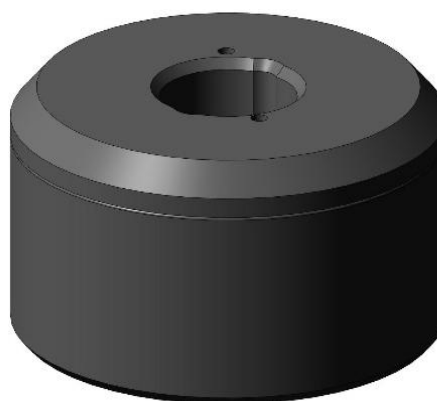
3D модель корпуса прессовой оснастки для прессования дугового канала времязадающего кольца ПИМа в сборе с двумя штифтами и кольцом
